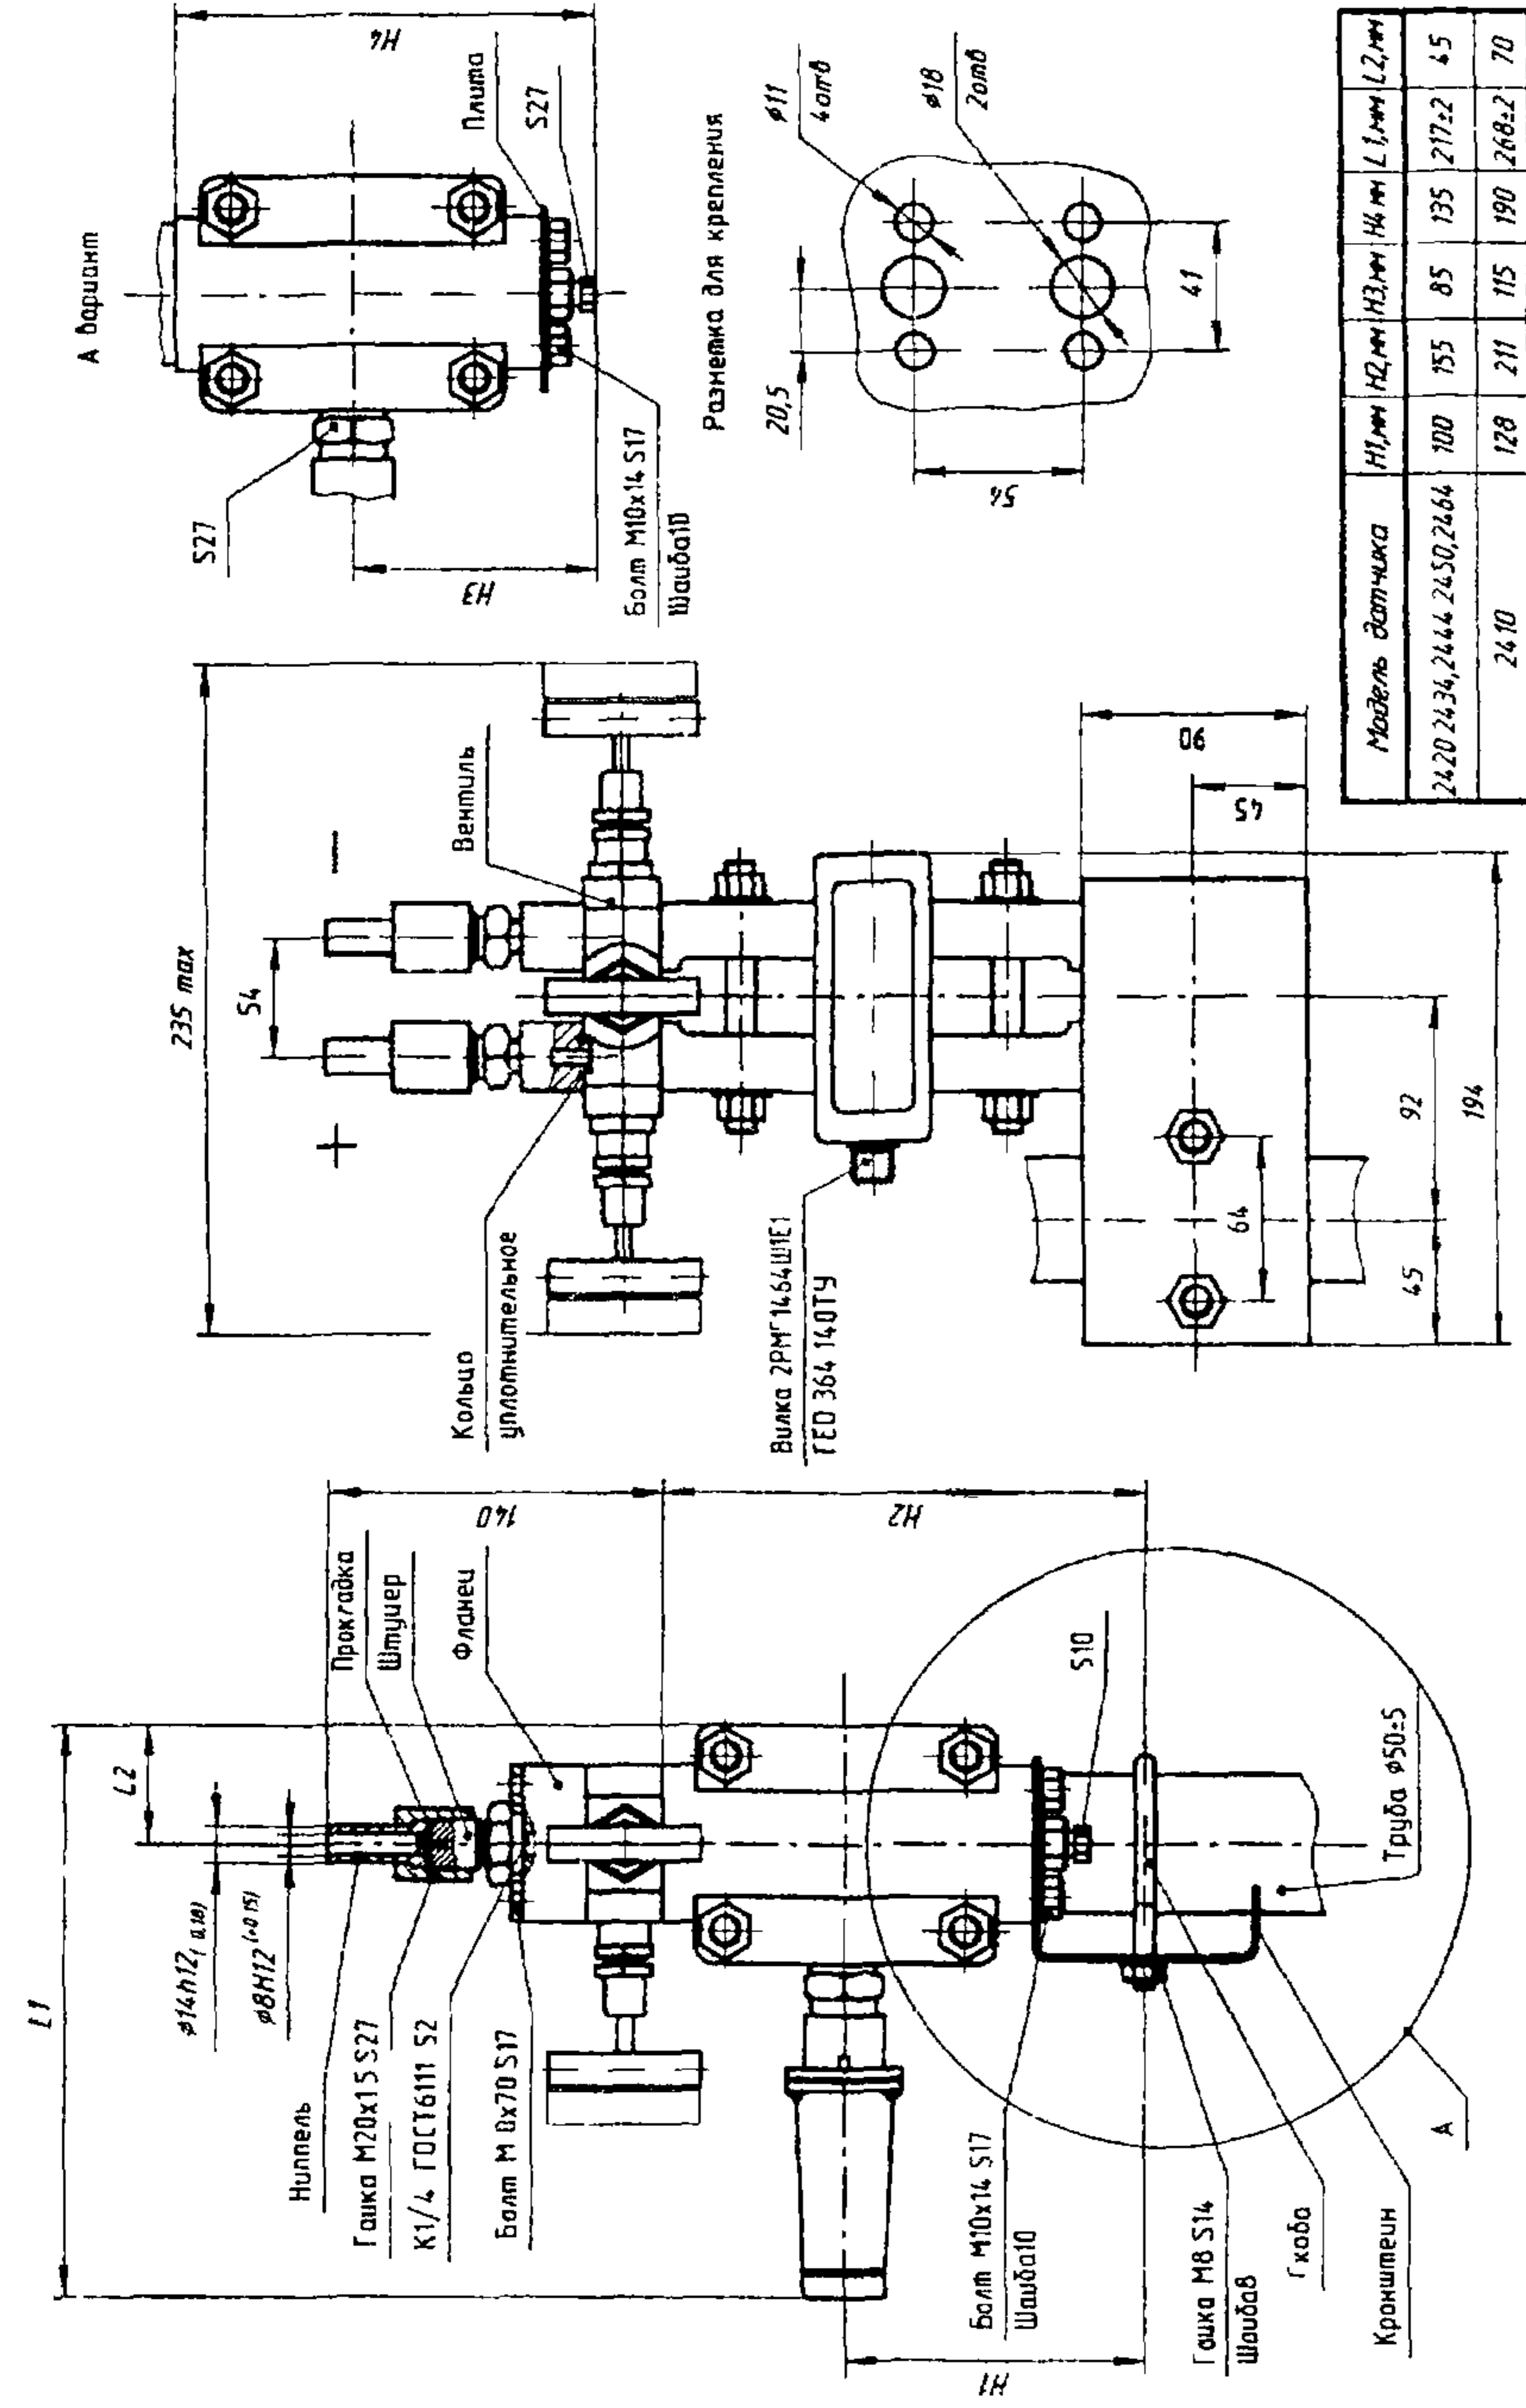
Установочные и присоединительные размеры датчиков модели 2410, 2420, 2434, 2444, 2450, 2464 с установленным трехвентильным блоком, ниппелями под наружные гайки
